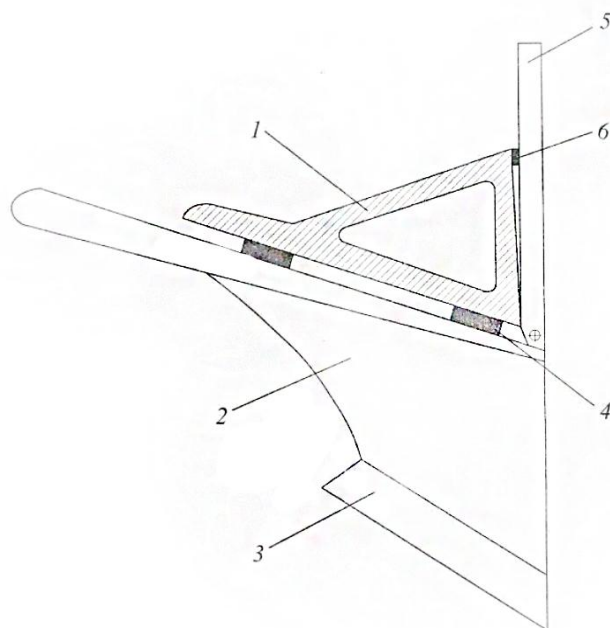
Корпус плуга з підпружиненою польовою дошкою [104]
